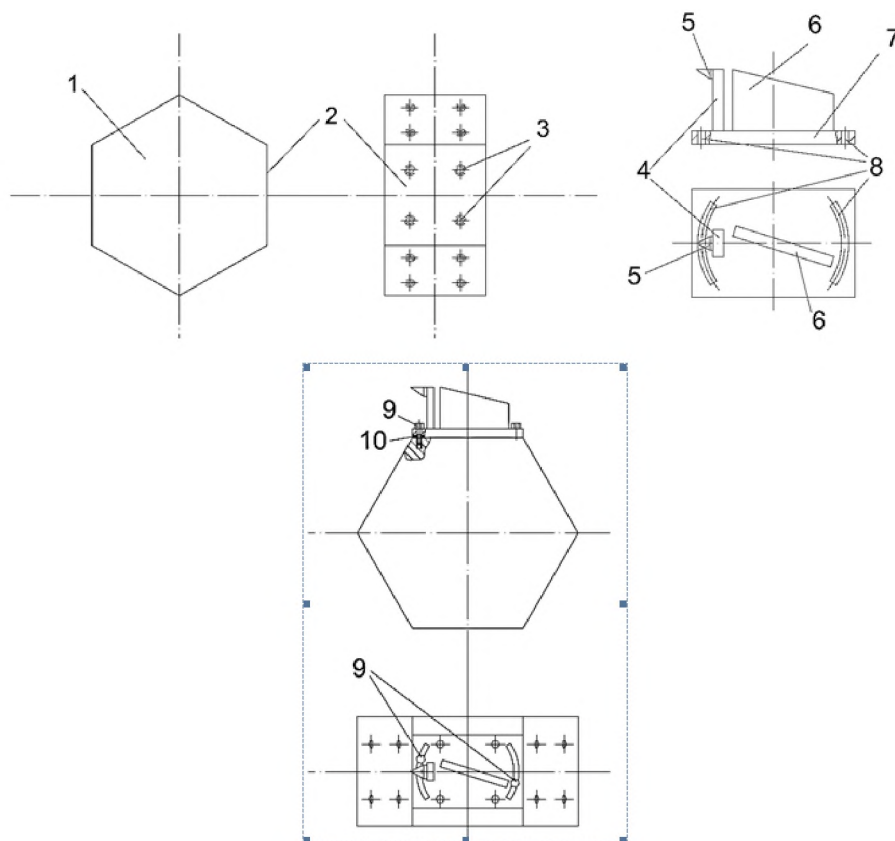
Узел крепления режущих элементов бесковшового ротора нижней разгрузки
